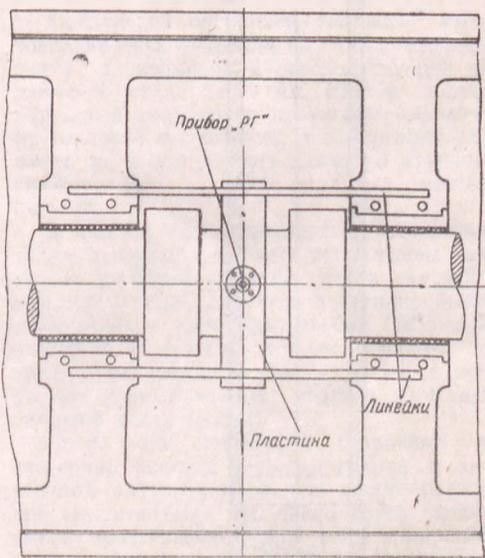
Вид в плане части рамы и коленчатого вала. Установка прибора при центровке цилиндрического блока.
